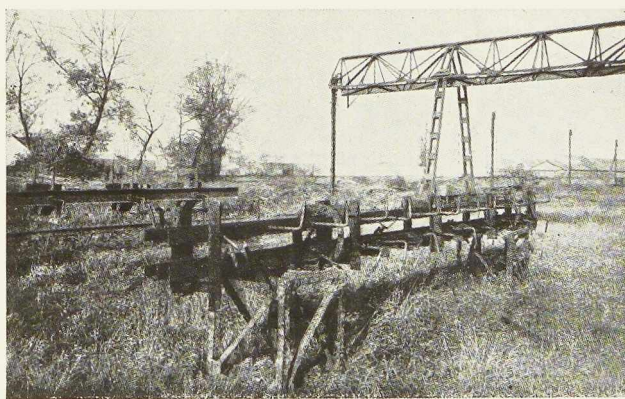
Dispositif pour l'assemblage par soudure des poutres en tôle du plancher.
